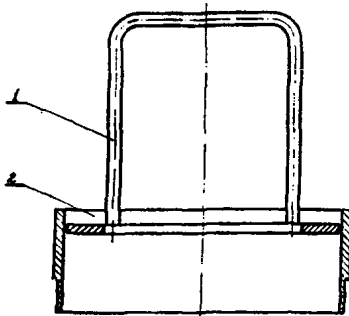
Приспособление для сборки скользящих контактов камеры:
